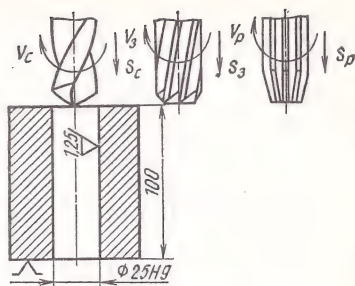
Эскиз обработки сверлением (размеры для варианта расчета)
